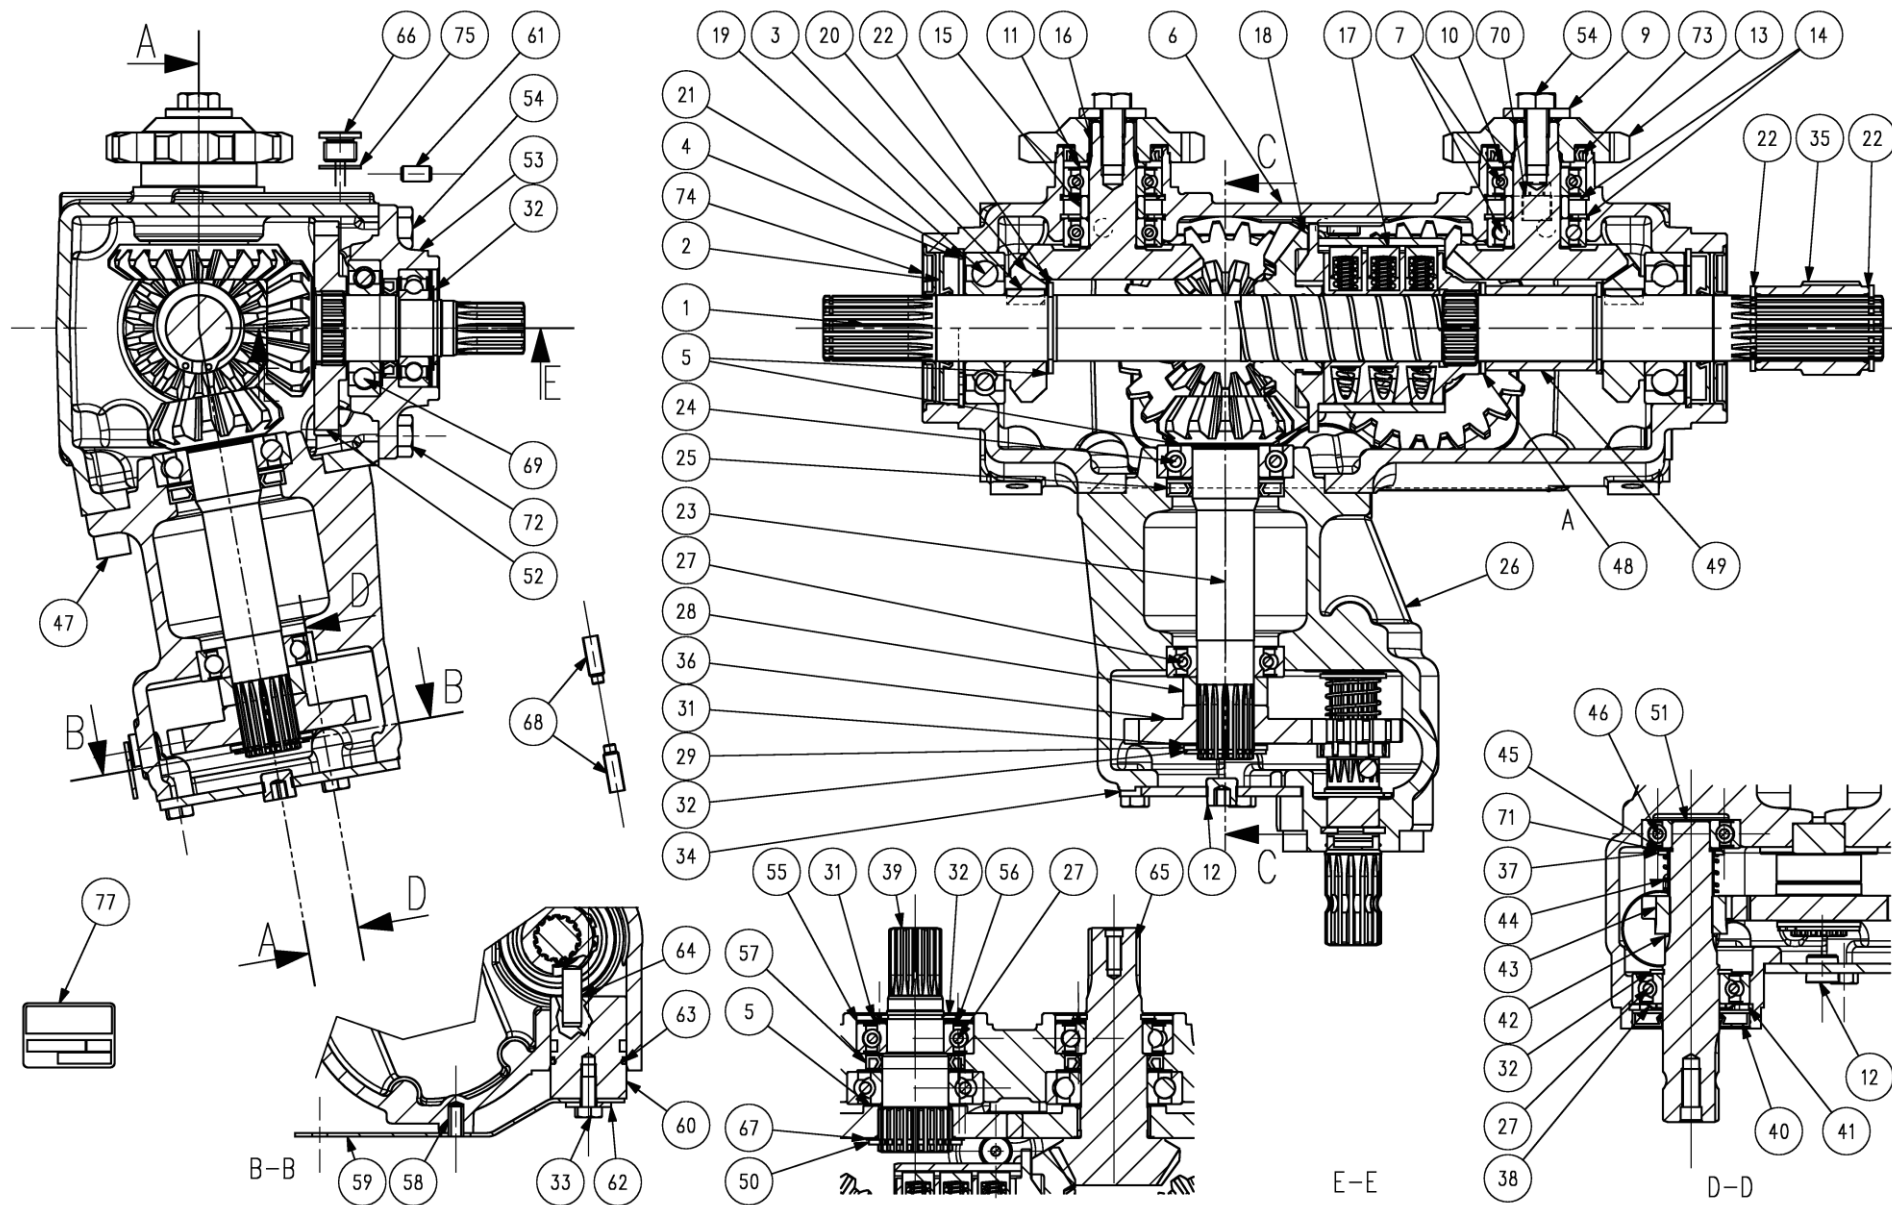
Редуктор русла правый 9.170.161.10 "Comer industries"
